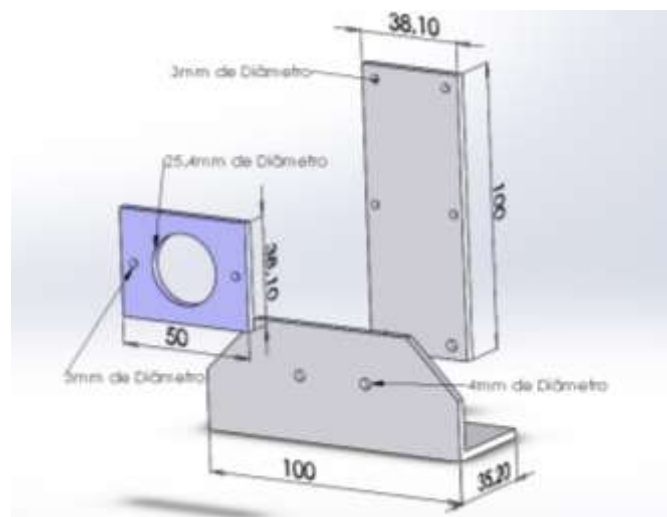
Suporte do espelho fixo. Vista explodida com medidas.
